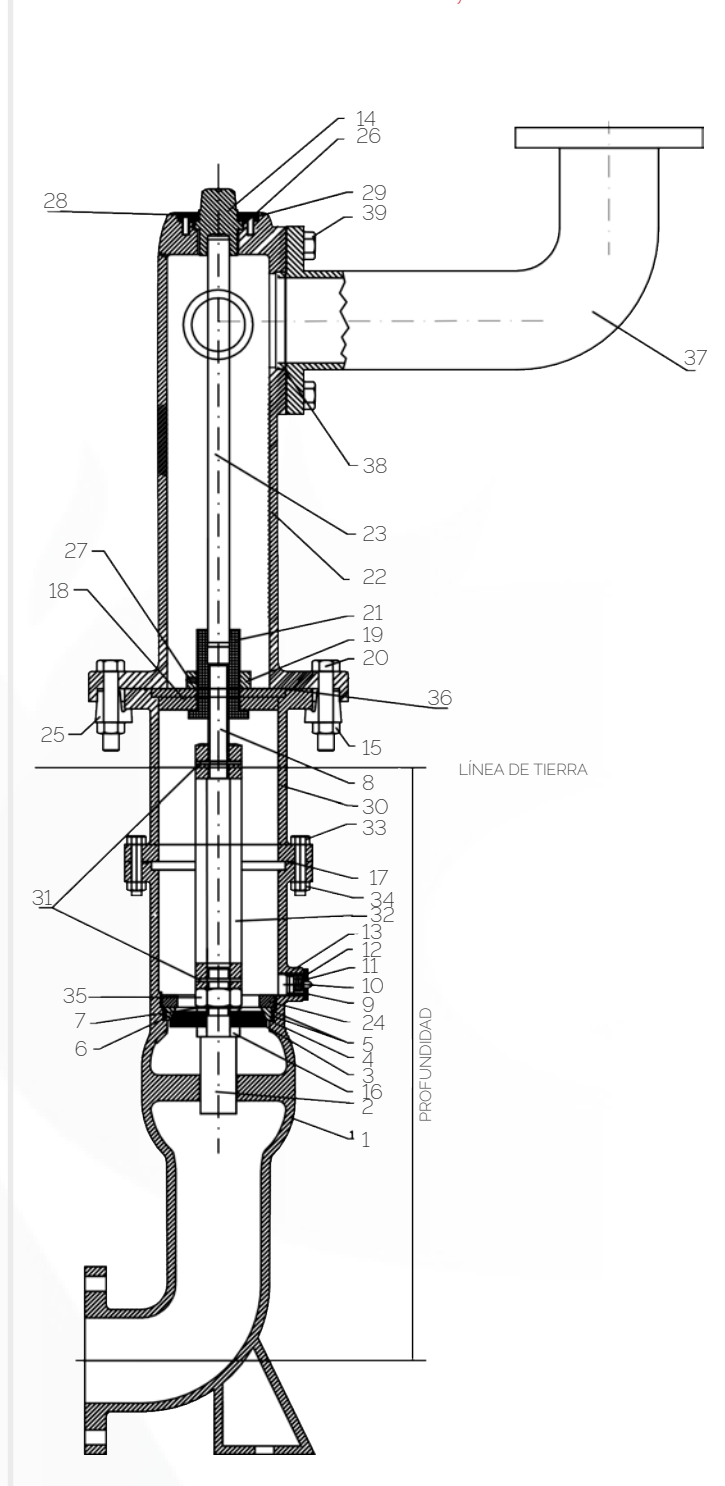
Plano TIFÓN CON TOMA y conexión Horizontal
